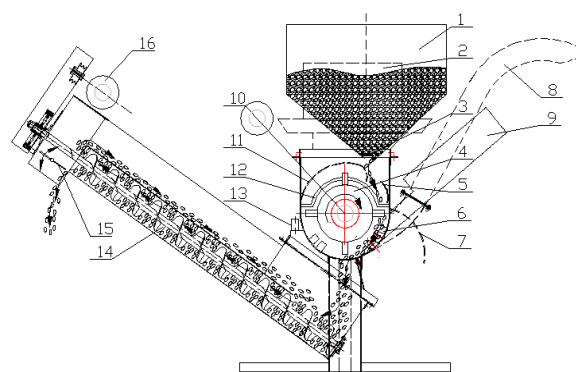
Схема универсального малогабаритного кормоприготовительного агрегата
